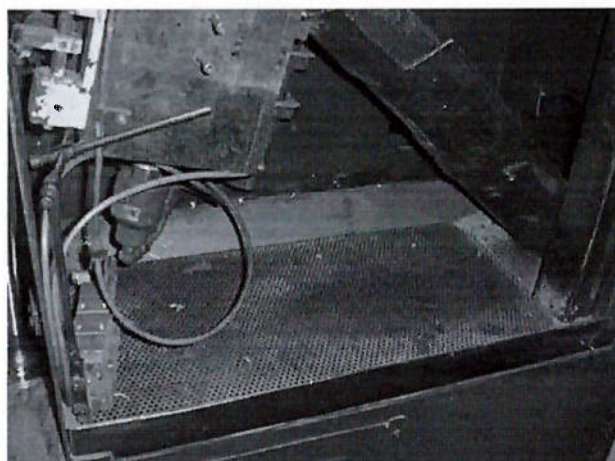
Chapa perfurada instalada no fundo da máquina.
